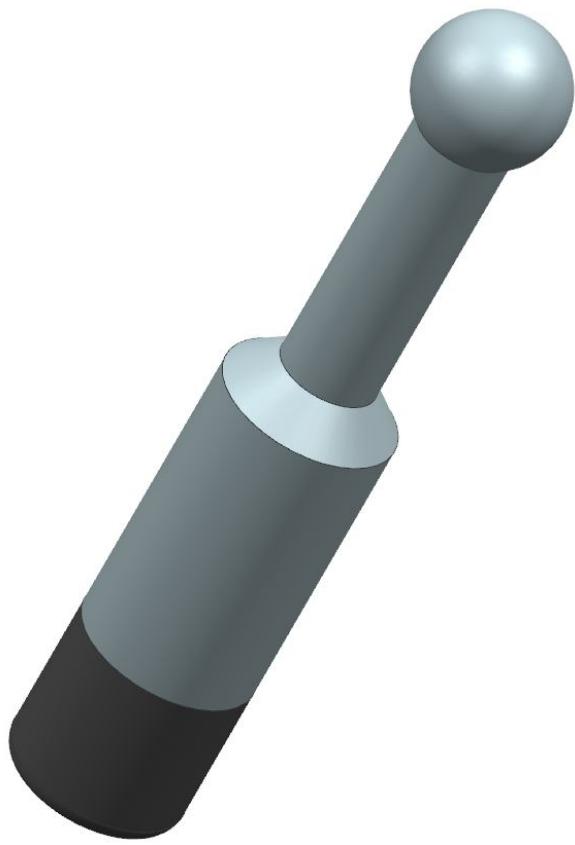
5-Ф-98, Оправка для установки поршневой группы в блок цилиндров
